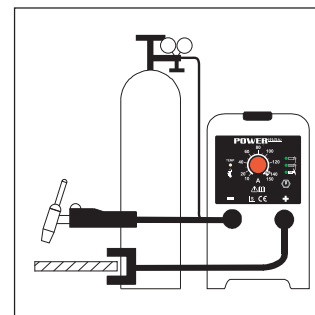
POWERmax équipé pour le soudage TIG
